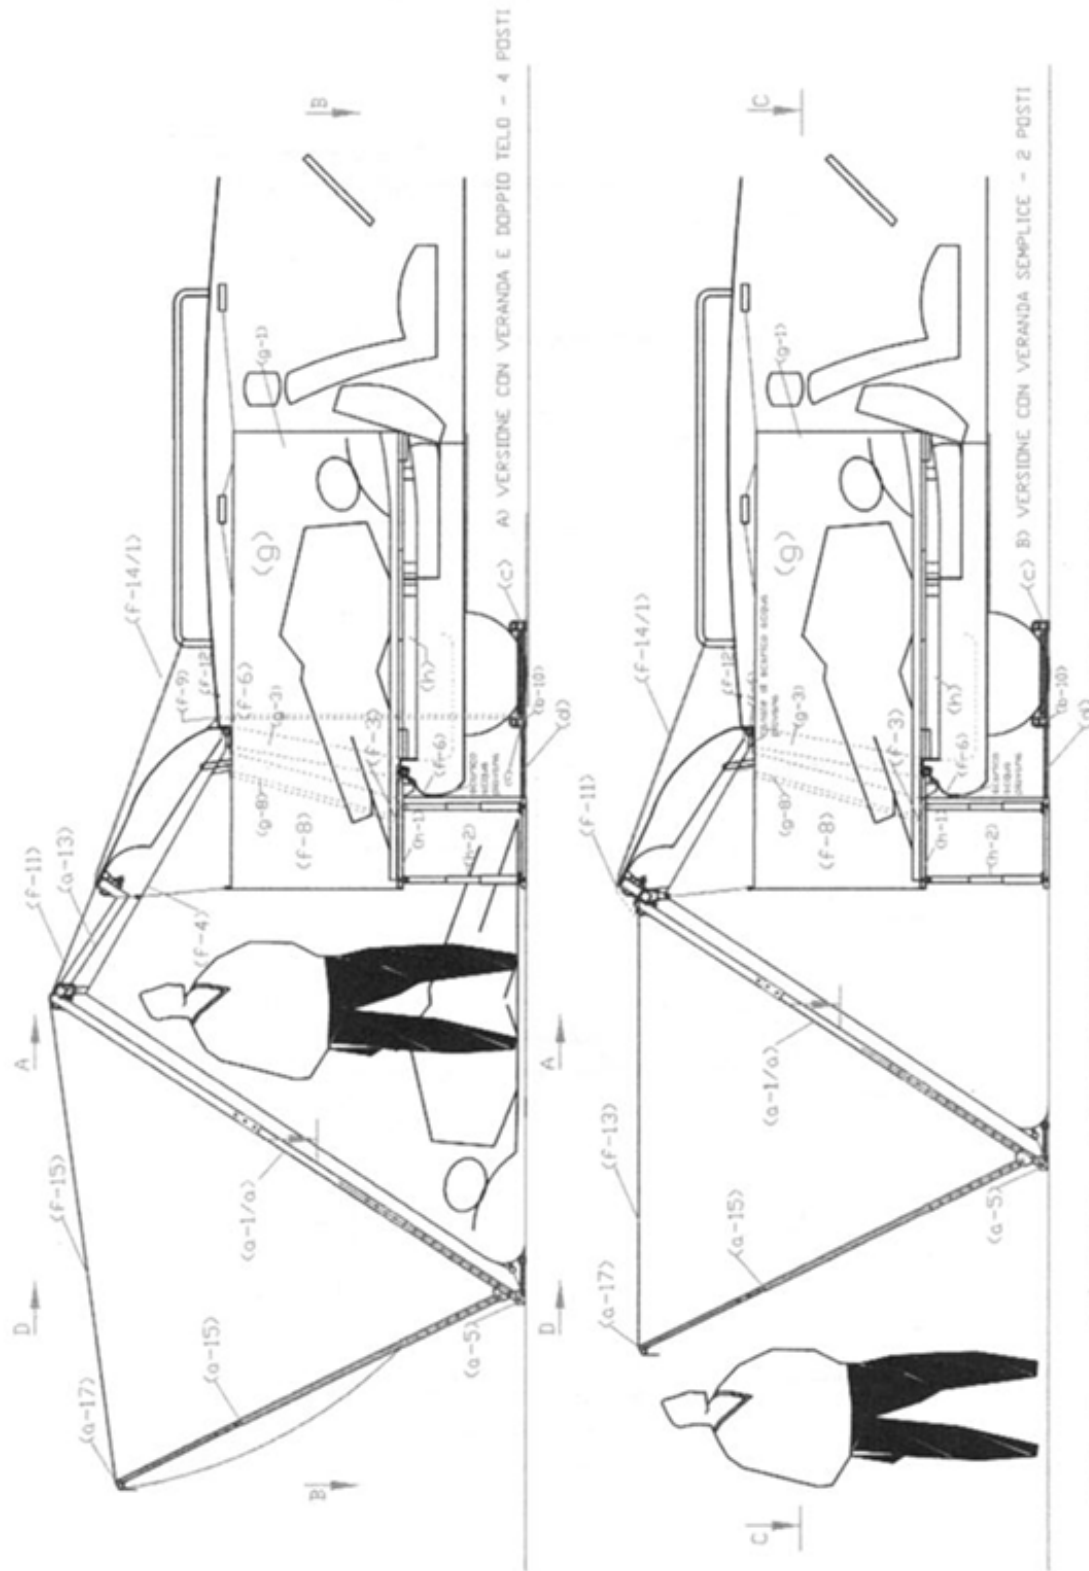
SEZIONI LONGITUDINALI AUTO CON TENDA A CASETTA
